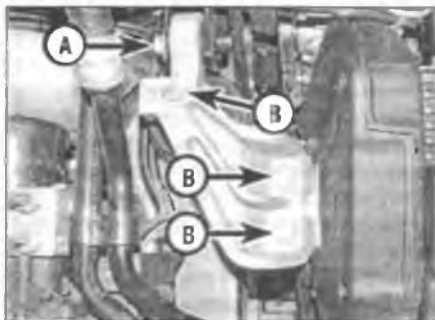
Болт верхней стяжки (А) и гайка/болты опорного рычага двигателя (В)
